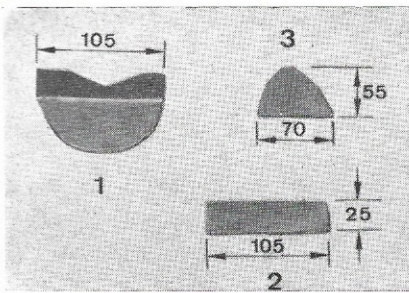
Pièces à confectionner pour fixation des feux arrière.
